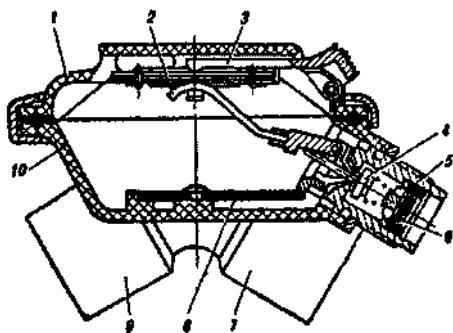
Дыхательный автомат аппарата АВМ-5: 1 — крышка, 2 — рычаг клапана, 3 — рычаг ручного привода, 4 — клапан, 5 — подводящий штуцер с седлом клапана, 6 — фильтр, 7, 9 — клапаны выдоха, 8 — отбойный щиток, 10 — корпус
